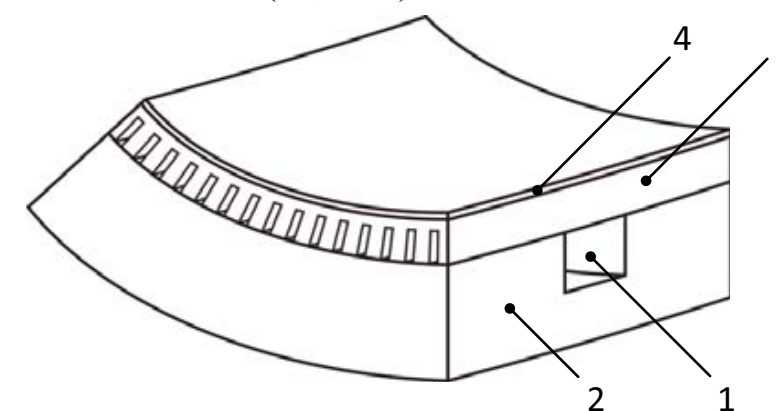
Технологический паз в корпусе камеры сгорания ракетного двигателя: 1 – технологический паз; 2 – ферромагнитный корпус; 3 – ячеистая неферромагнитная прослойка; 4 – никелевое покрытие
